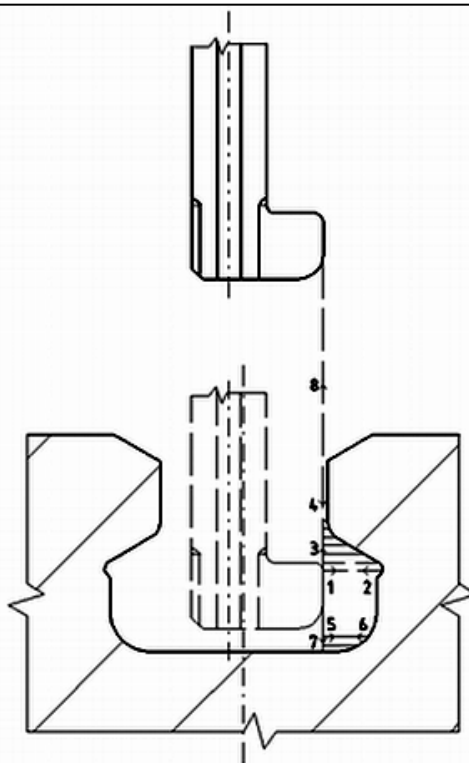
Dráhy nástroje při soustružení krčku a kapsy drážky
